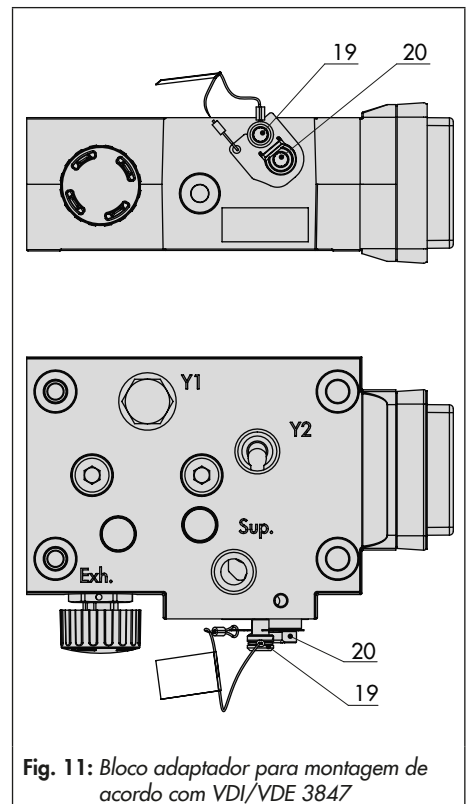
Bloco adaptador para montagem de acordo com VDI/VDE 3847
